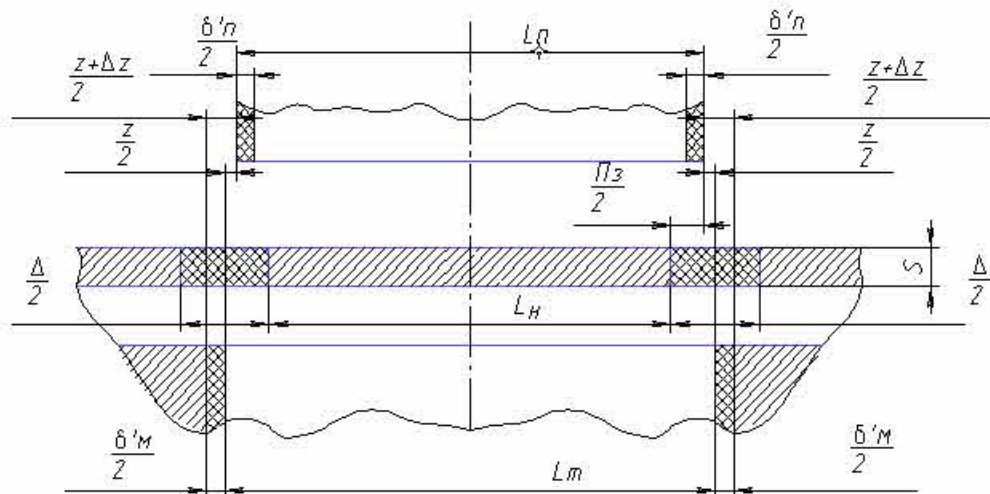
Схема розмірів і полей допусків елемента, що штампується і робочих деталей штампа при їх роздільному виготовленні для операції пробивання отвору:  $L_n$  – номінальний розмір елемента, що штампується;  $L_p$  – номінальний розмір пуансона;  $\Delta$  – допуск розміру елемента, що штампується;  $\Pi_n$  – припуск на знос пуансона і матриці;  $\delta_p$  і  $\delta_m$  – допуски розмірів пуансона і матриці;  $z$  і  $\Delta z$  – зазор і поле допуску зазору між матрицею і пуансоном.
